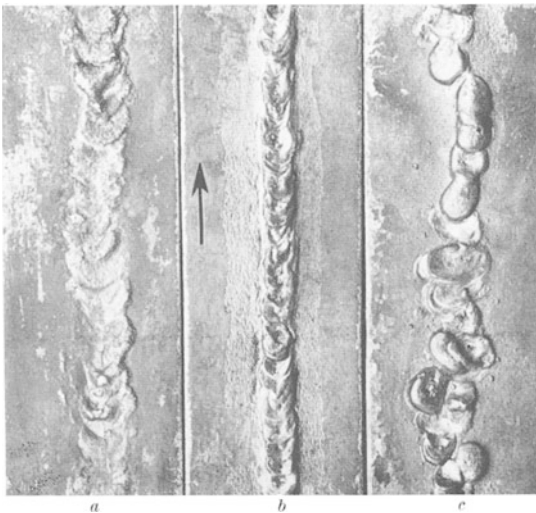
Fehlerhafte Schweißnähte an 1 mm-Stahlblechen.
